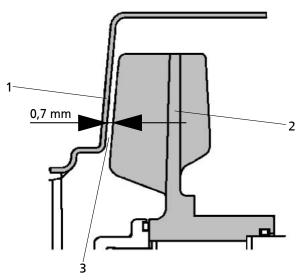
Holgura axial entre la carcasa de la bomba y el rodete
